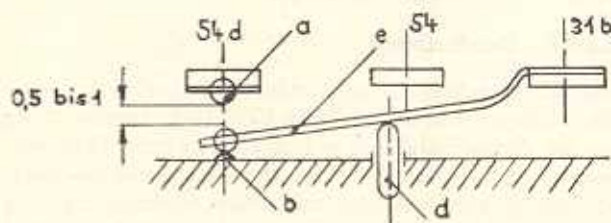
Ansicht von hinten gegen die Anschlußplatte mit Endausschalter
